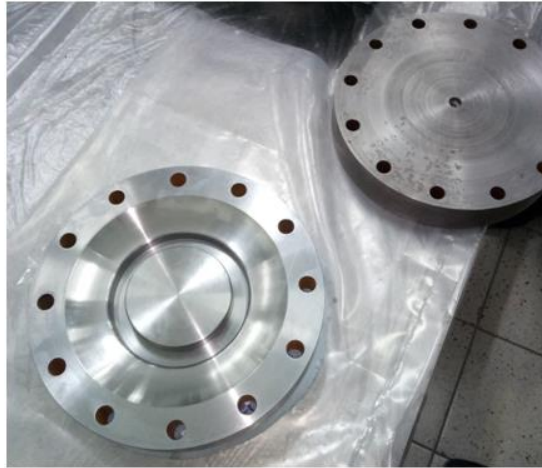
Прес-форма для виготовлення заготовки фланця
